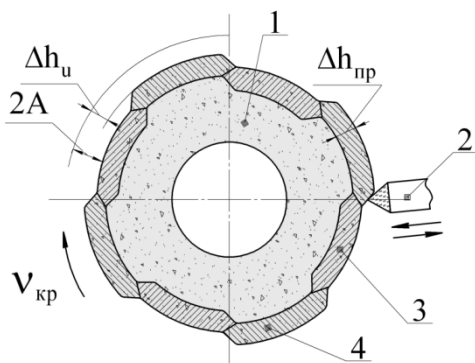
Схема правки шлифовального круга с прерывистой рабочей поверхностью
